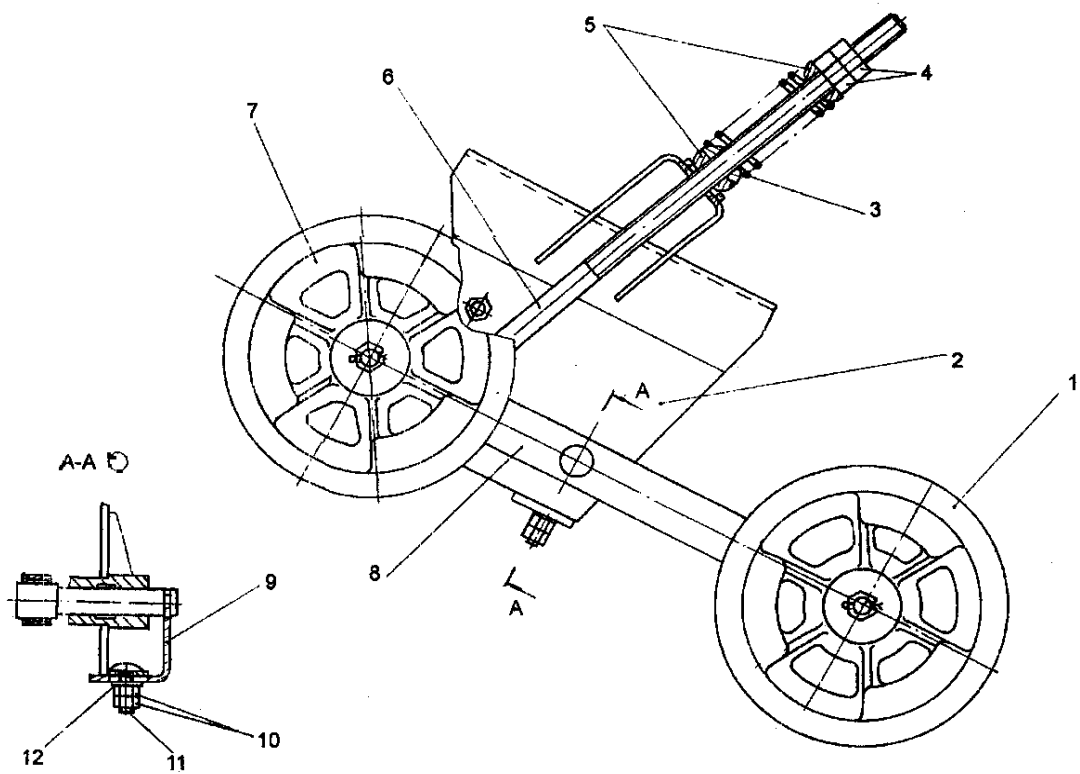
Натяжное устройство: 1, 7 – шкивы; гайка; 2 – опора; 3 – пружина; 4 – гайки; 5 – шайбы сферические; 6 – тяга; 8 – рычаг; 9 – кронштейн; 10 – гайки; 11 – болт; 12 – шайба
